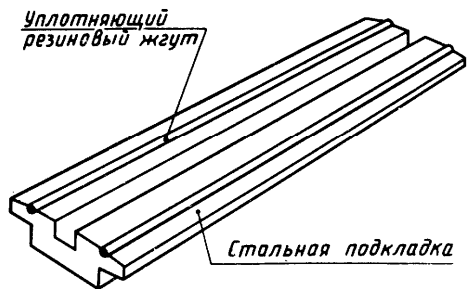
Детали уплотнения для защиты обратной стороны сварного шва
